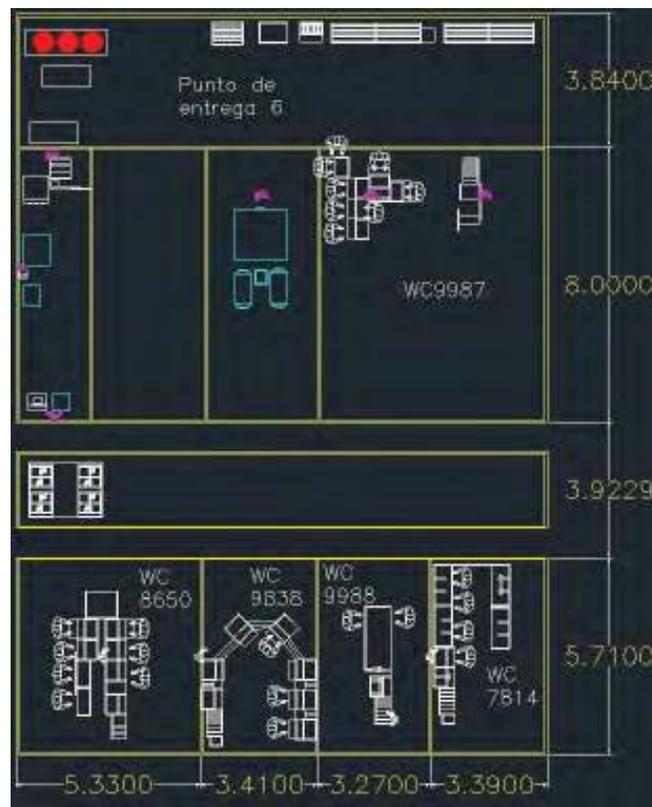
Medidas de la distribución de planta (Elaboración propia, 2017).
